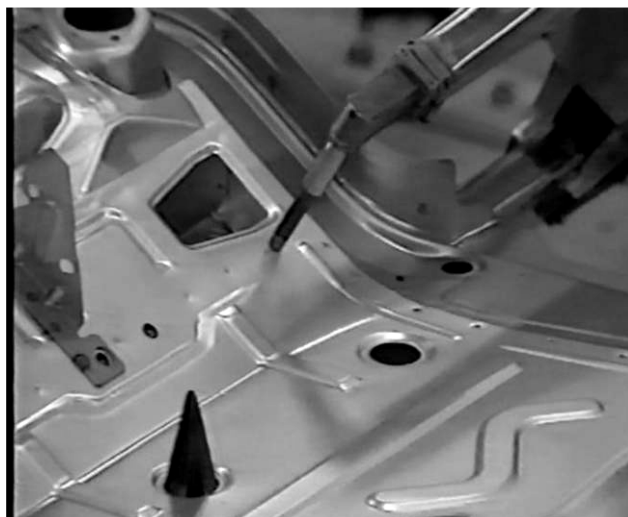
Точечная рельефная сварка на автоматических сварочных машинах
